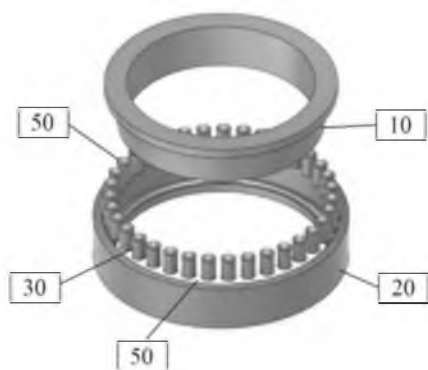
3D-модель модернизированного радиального подшипника с роликовыми цилиндрическими телами качения
